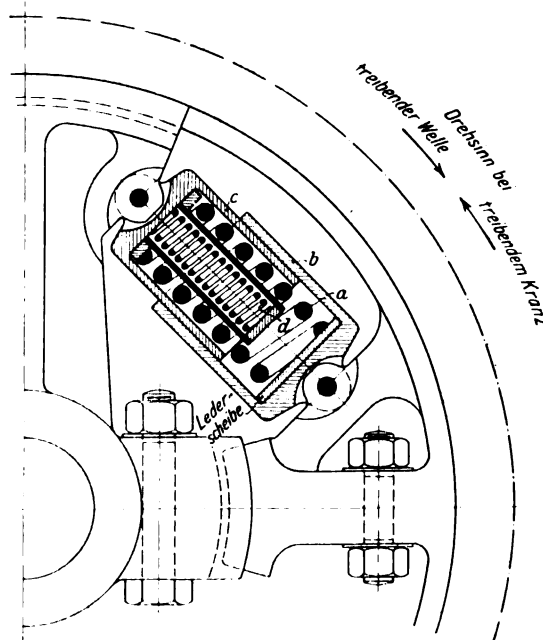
Elastisches Zahnrad mit Druckfeder.
